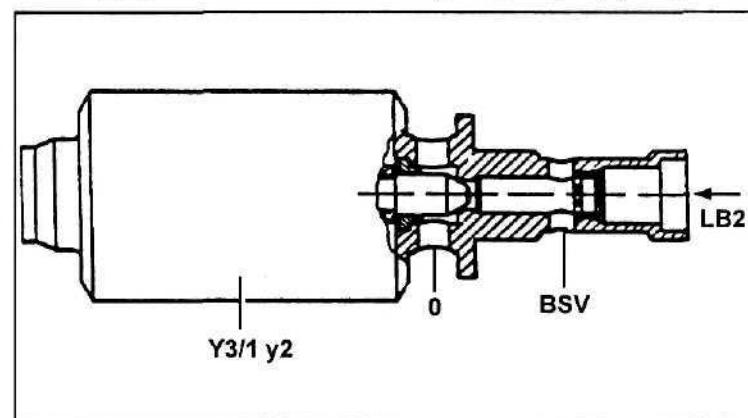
Регулировочный клапан (соленоид) Y3/1y2.
